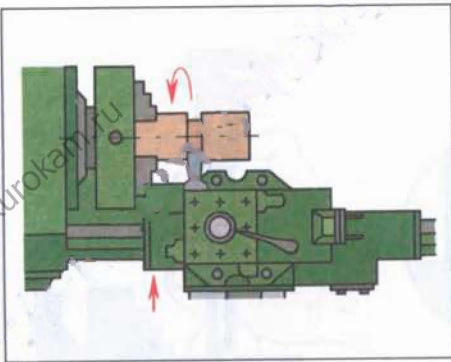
Режущая кромка резца располагается параллельно оси центров
